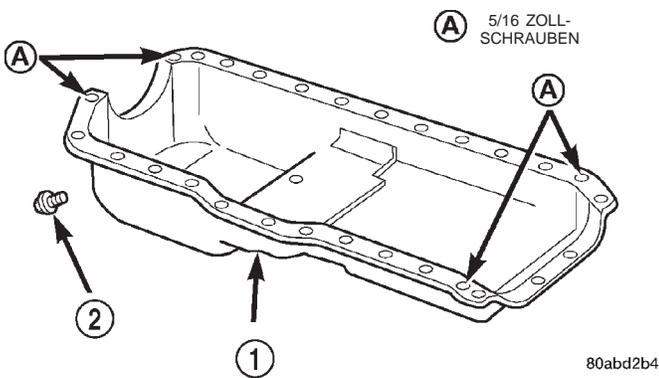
Lage der 5/16 Zoll-Ölwannenschrauben
